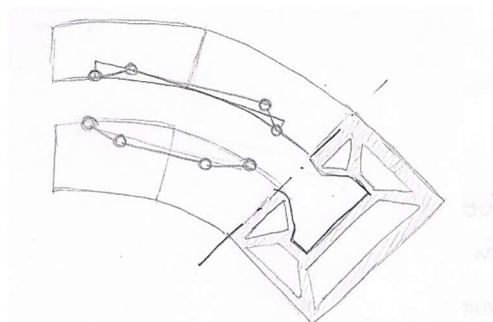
Detalle lateral de estructura hueca de las piezas
